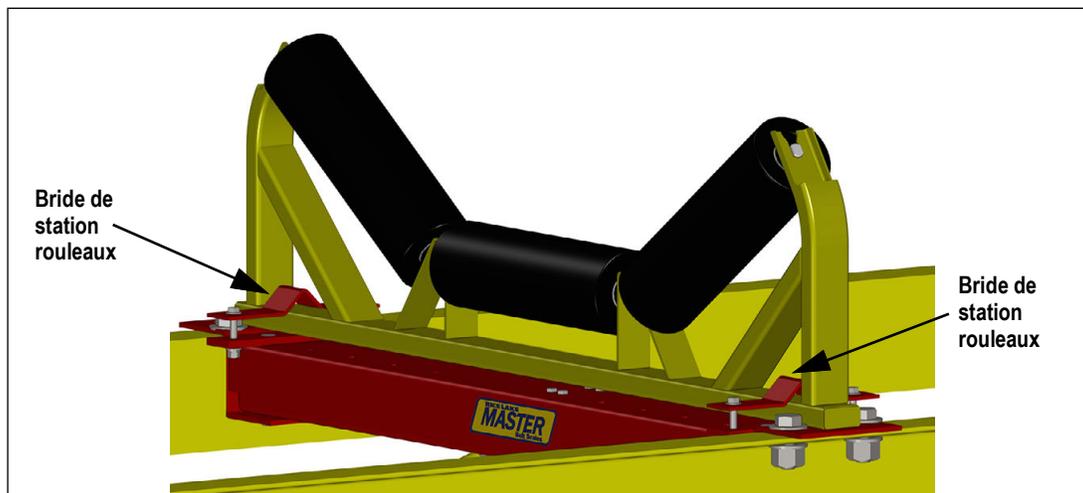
Installez la station rouleaux sur la barre peseuse
